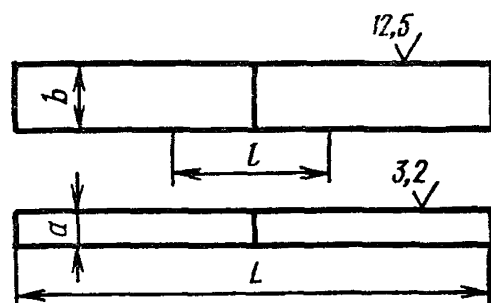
Образец для испытания сварного соединения на статический изгиб
